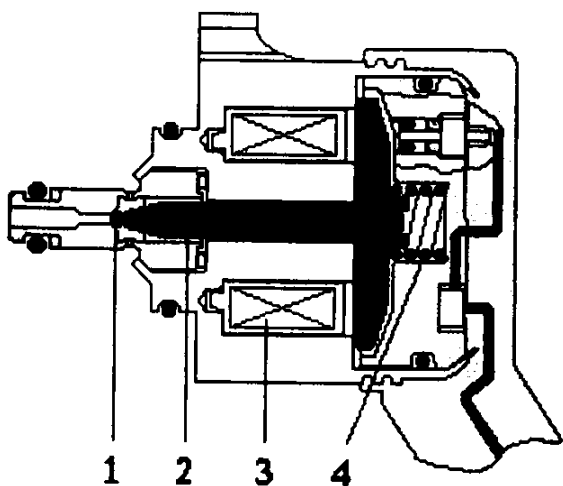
Електрокерований редукційний клапан CR Bosch
